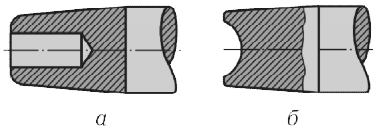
Інструменти для клепаання: а – натяжка; б – обтискання
